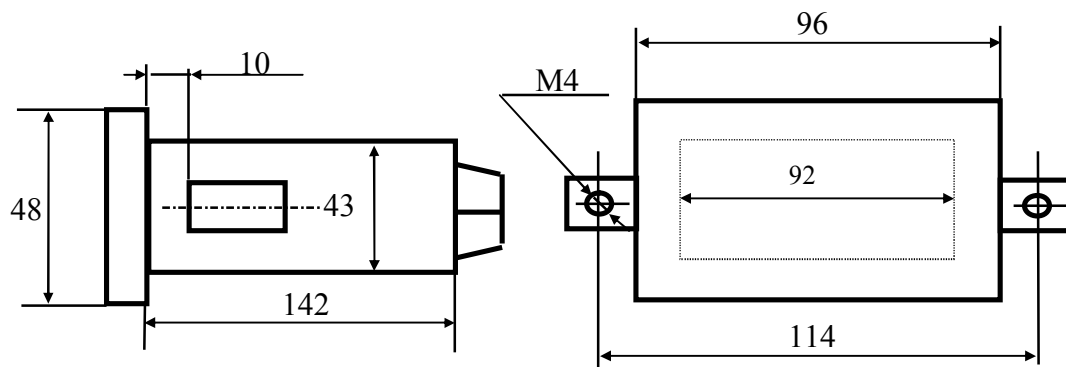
а Габаритные размеры, корпус 48x96x155 мм.
